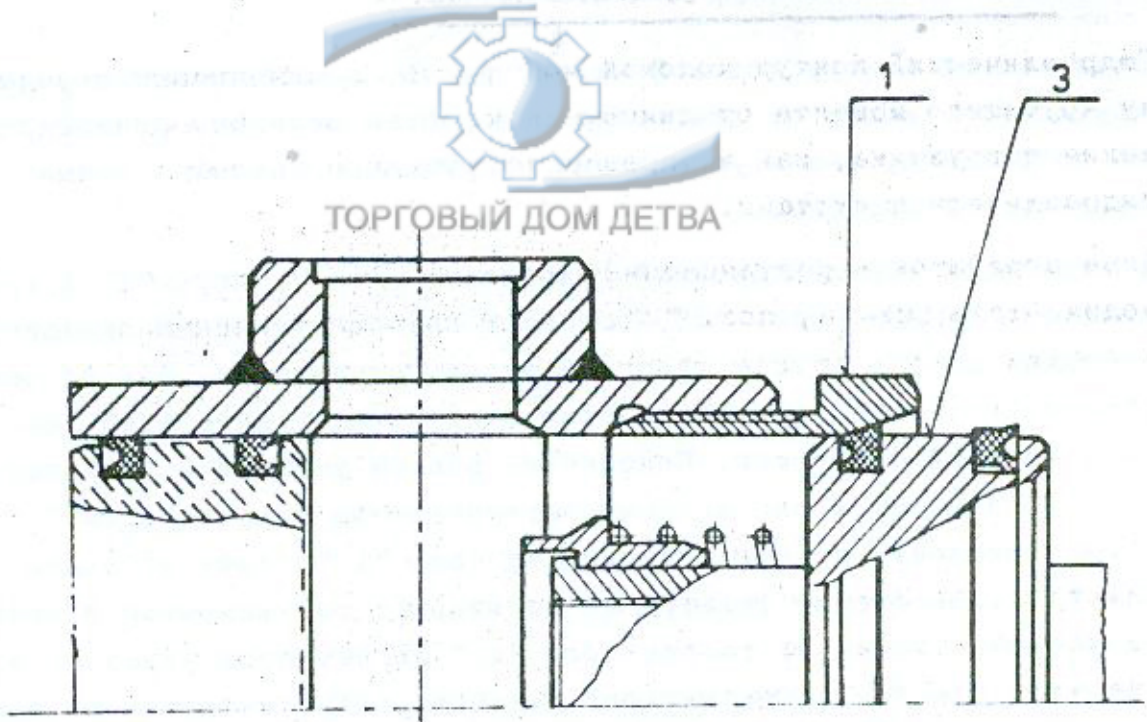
Монтаж поршня с поршневым штоком в корпус прямолинейного гидродвигателя с помощью приспособлений
